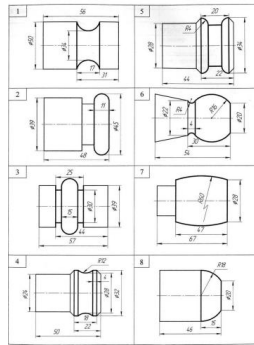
Эскизы деталей для обработки фасонной поверхности
